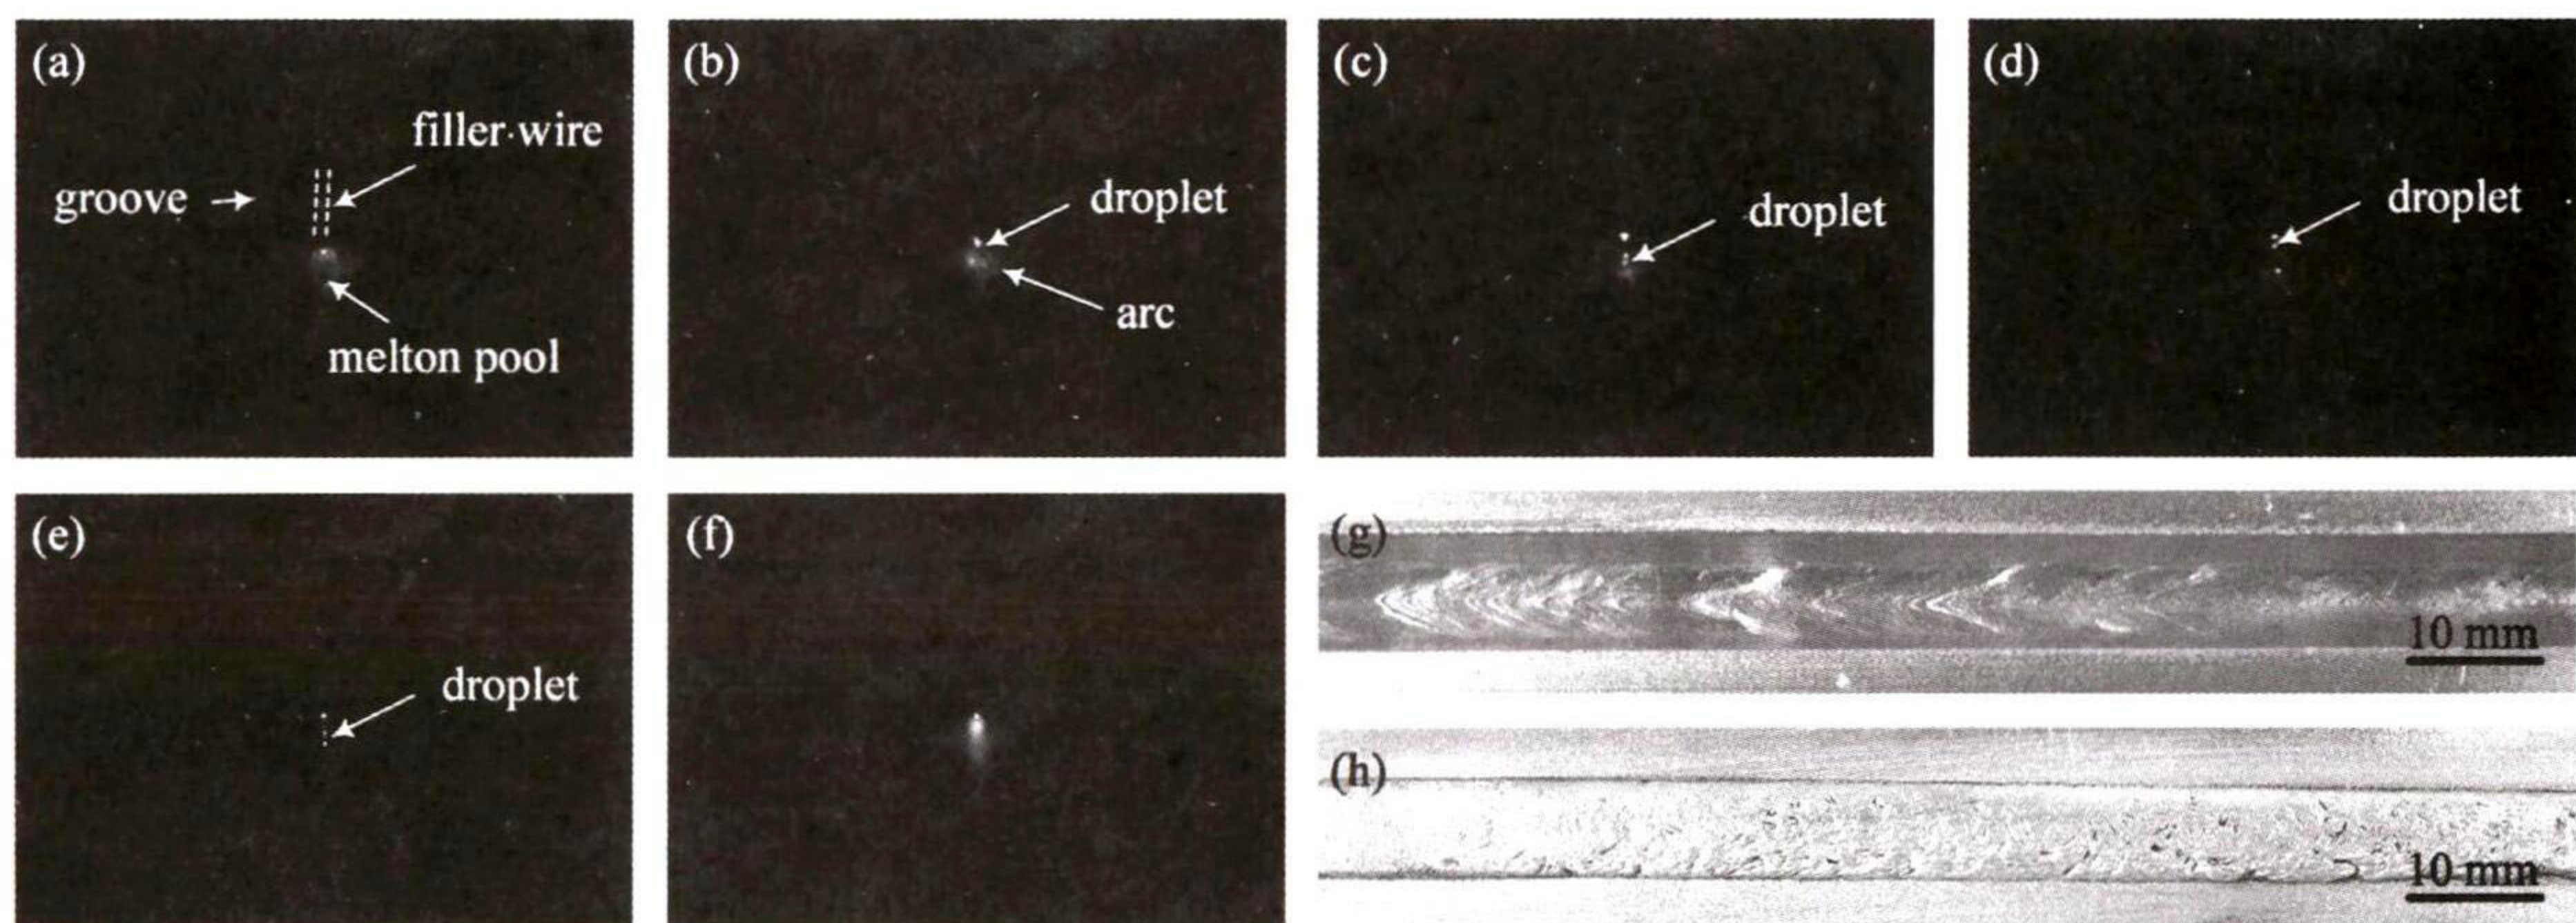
焊接速度0.8 m/min时的熔滴过渡、电弧形态和焊缝成形特征
